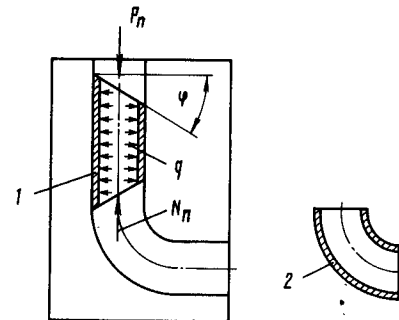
Схема гибки короткой трубы проталкиванием через торoidalный канал разъемной матрицы:
